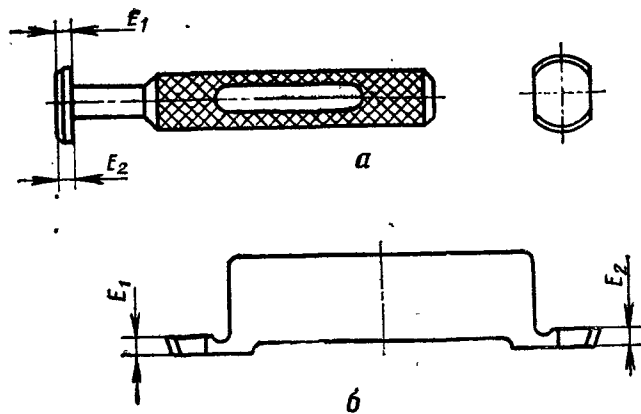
Калибры для проверки расстояния от дна чашечки затвора до зацепа выбрасывателя:
